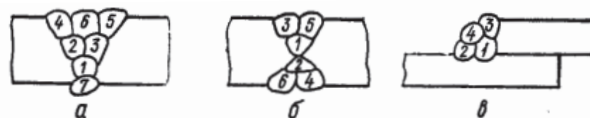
Порядок укладки сварочных прутков в шов: а – стыковой V-образный шов, б – стыковой X-образный шов, в – нахлесточное соединение
